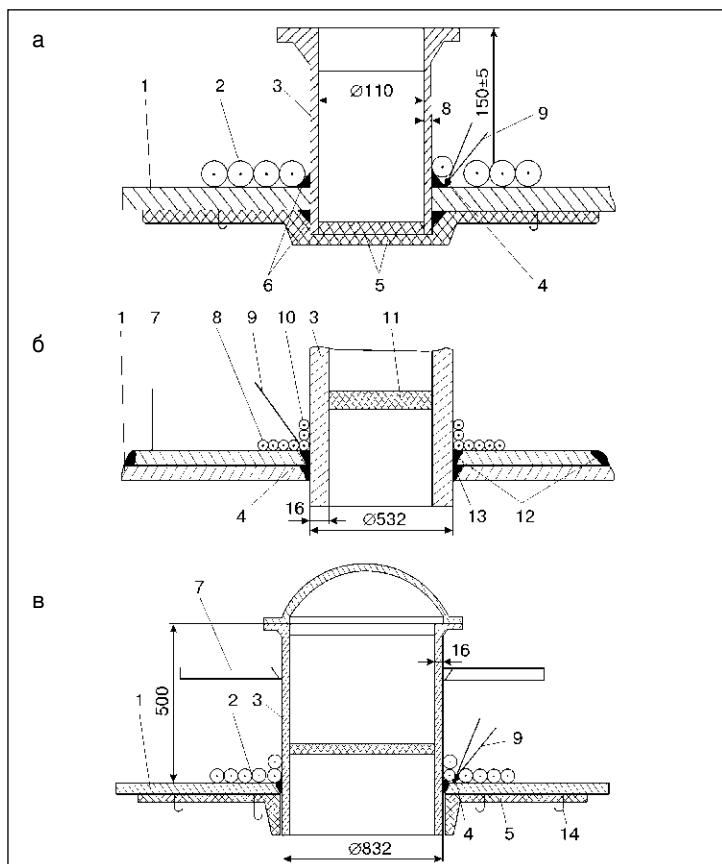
Схемы установки электронагревателей при местной термообработке сварных соединений штуцеров и люков-лазов сферического резервуара жидкого аммиака вместимостью 2000 м³: а — штуцеры; б — люк-лаз диаметром 532 мм; в — люк-лаз диаметром 832 мм (1 — верхняя крышка; 2 — витки электронагревателя КЭН-3; 3 — штуцер или люк-лаз; 4 — место установки термоэлектрического преобразователя; 5 — внутренняя теплоизоляция; 6 — сварной шов; 7 — воротник; 8 — электронагреватель ГЭН на воротнике; 9 — термоэлектрический преобразователь; 10 — электронагреватель ГЭН на штуцере; 11 — заглушка; 12 — сварные швы воротника; 13 — сварные швы верхней крышки; 14 — крючки для крепления теплоизоляции)
